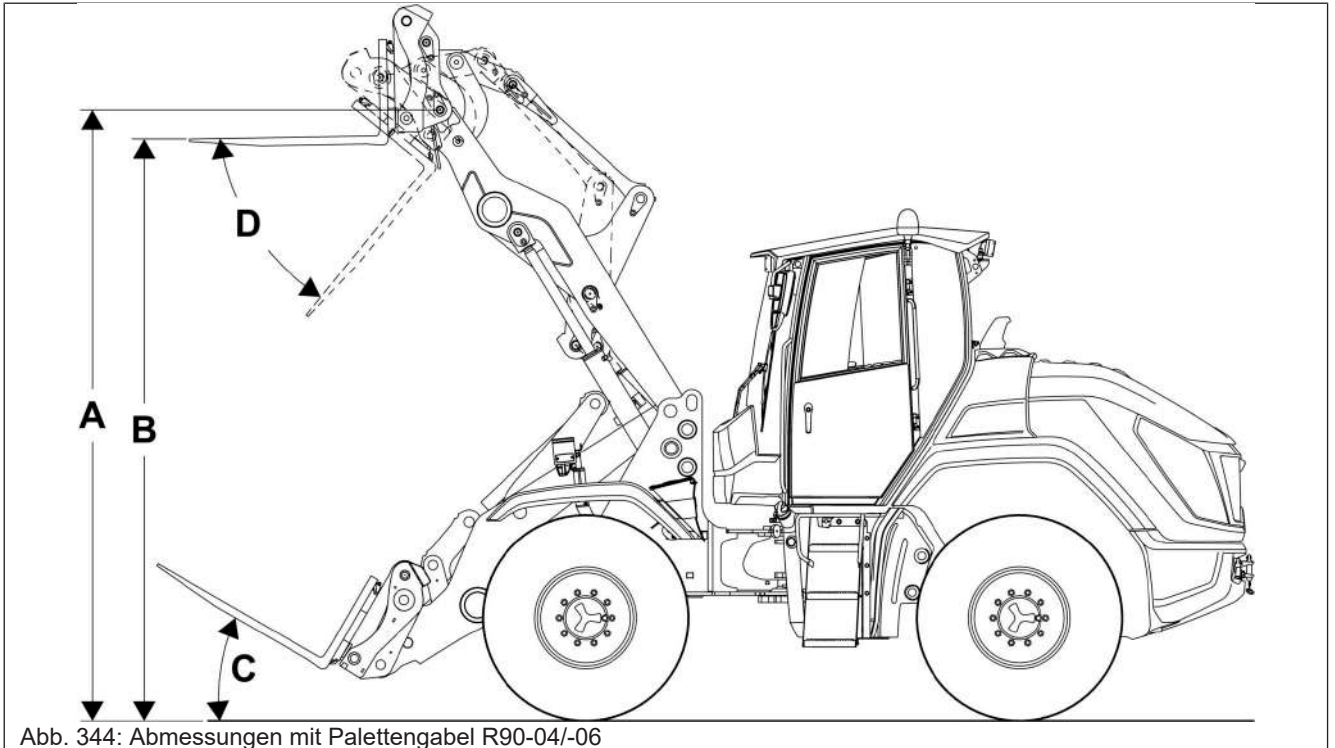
Abmessungen mit Palettengabel R90-04/-06
